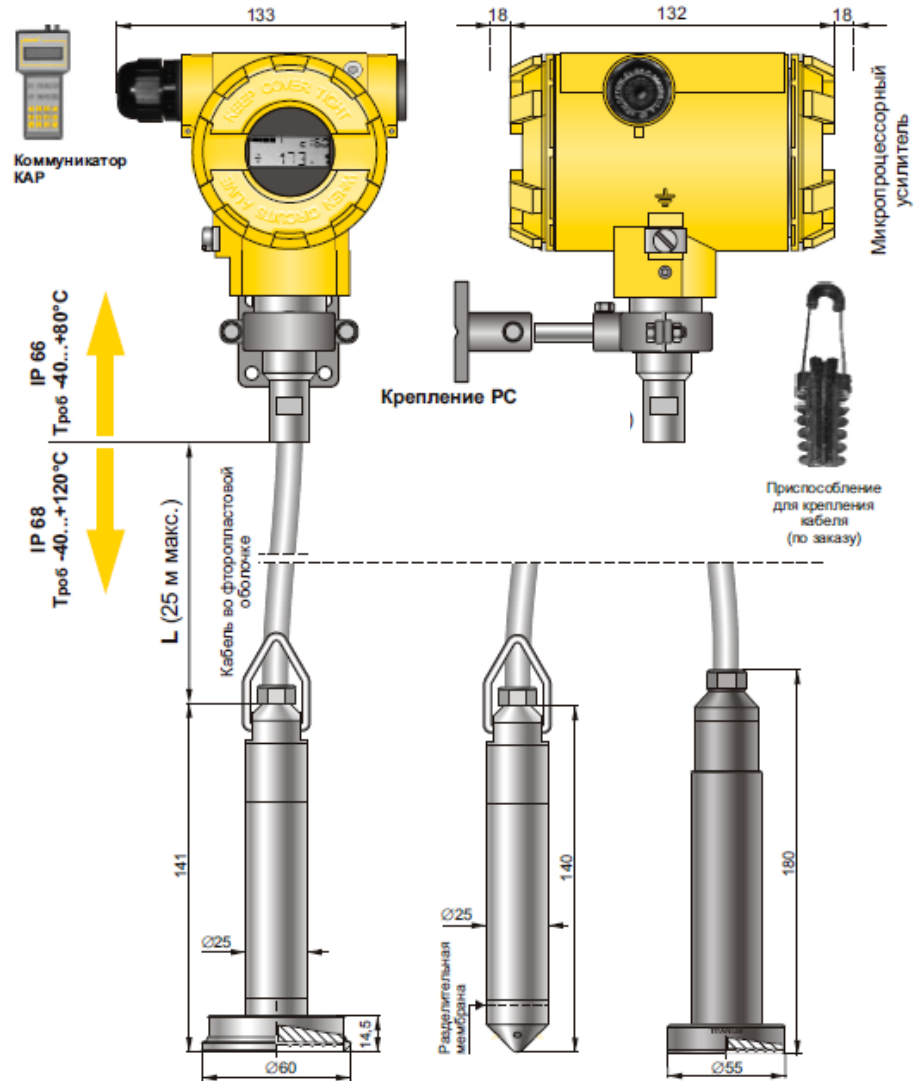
Внешний вид, установочные и присоединительные размеры преобразователей PC-SG-25.Smart/ALW, PC-SG-25S.Smart/ALW
